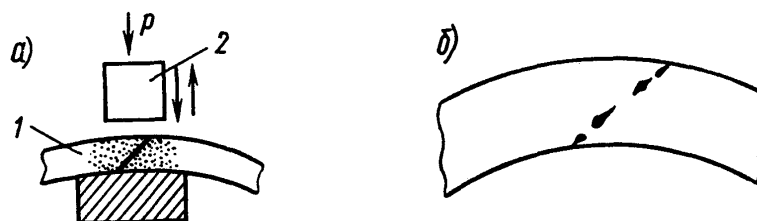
Схема ковальського (пічного) зварювання:
